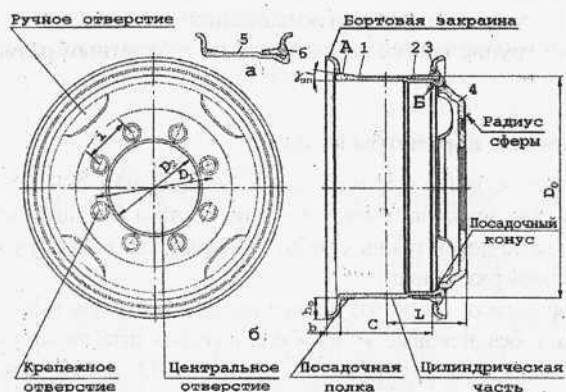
Основные параметры дискового колеса: а – двухкомпонентный обод; б – трехкомпонентный обод; 1, 5 – основание обода; 2 – замочное кольцо (разрезное); 3 – бортовое кольцо (неразрезное); 4 – диск; 6 – бортовое кольцо (разрезное); А – посадочная полка; Б – коническая поверхность ($\gamma_{п.п} = 28^\circ$); в – ширина бортовой закраины; С – ширина обода; L – вылет диска; D₁ – диаметр крепежных отверстий; D₂ – внутренний диаметр диска; $\gamma_{пл} = 5^\circ$ – угол наклона посадочной полки; h₃ – высота бортовой закраины
